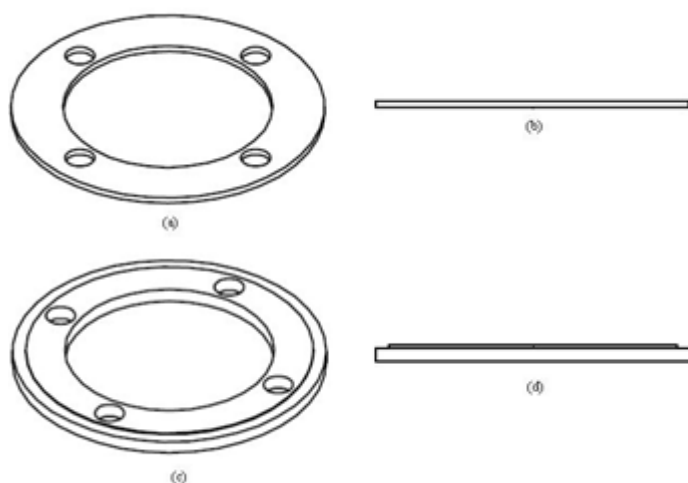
Prospetto (a) dall'alto e (b) laterale della ghiera usata per il fissaggio delle membrane; prospetto (c) dall'alto e (d) laterale della ghiera usata come supporto. Quest'ultima è costituita da uno scanso, visualizzabile nel prospetto laterale, sui sono state disposte le membrane.
